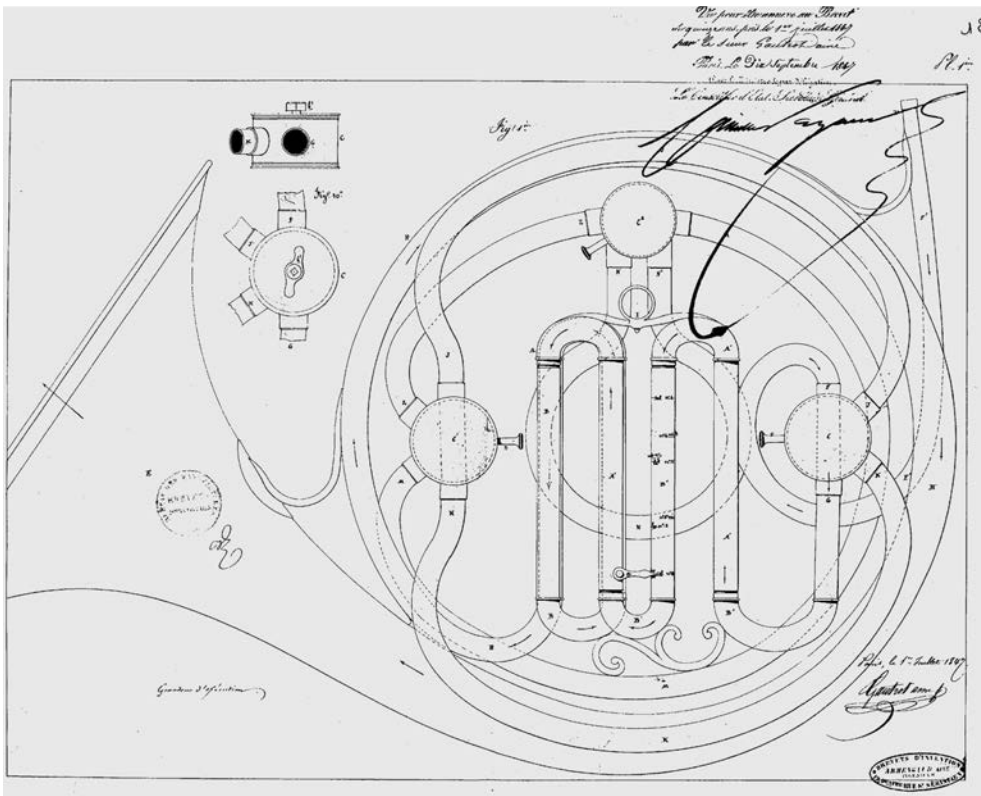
Dessin du brevet 5874 du 1^{er} juillet 1847, planche 1
